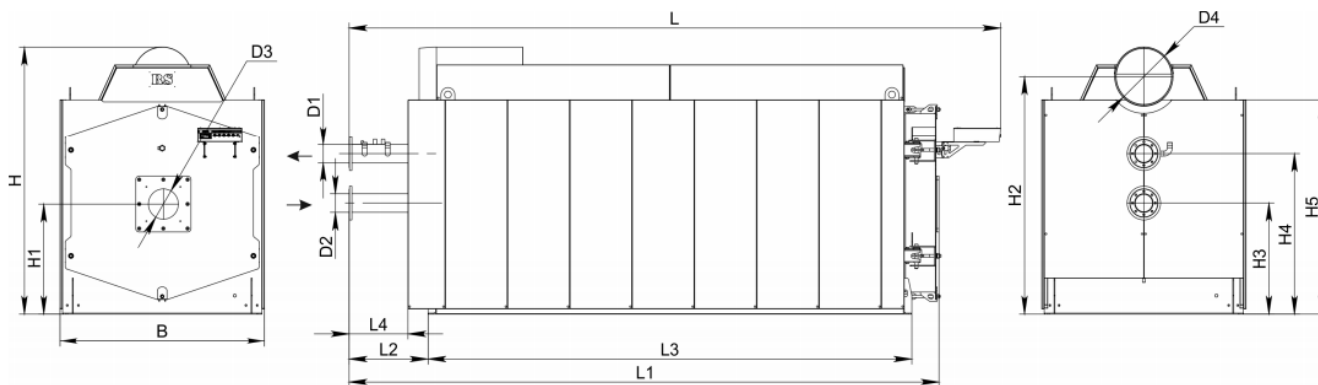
Габаритные размеры котла Rossen RS-D 3500:
